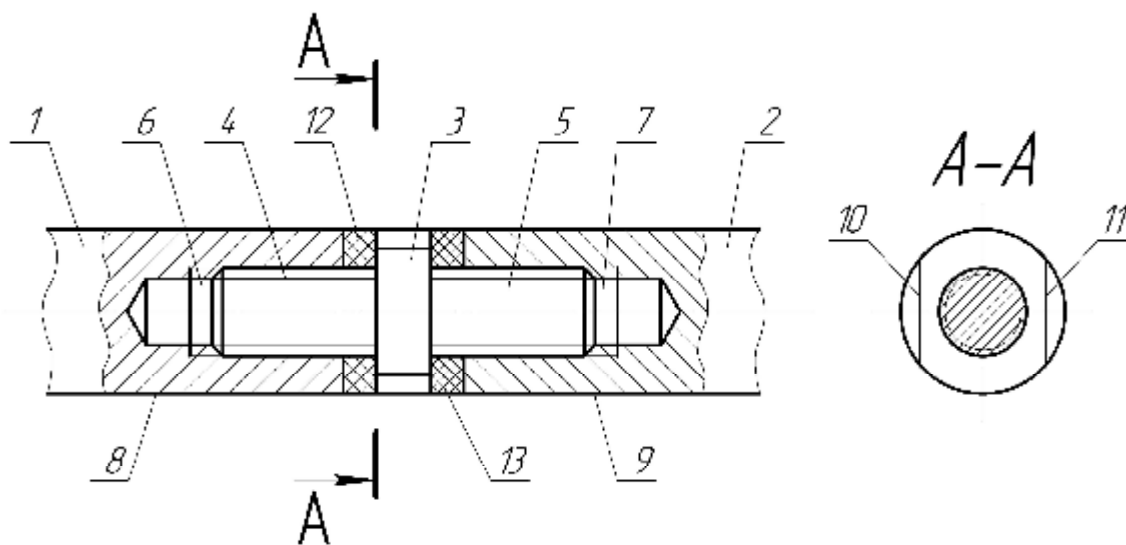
Схема різьбового з'єднання валів з засобом для з'єднання та фрикційними шайбами: 1 – ведучий вал; 2 – ведений вал; 3 – засіб для з'єднання валів; 4, 5 – різьбові стержні; 6, 7 – різьбові отвори; 8, 9 – поверхні відповідно ведучого та веденого валів; 10, 11 – лиски; 12, 13 – фрикційні шайби
